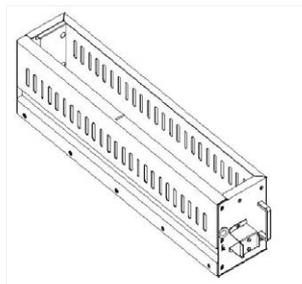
Instalación de baterías 1: extraiga la caja de baterías
